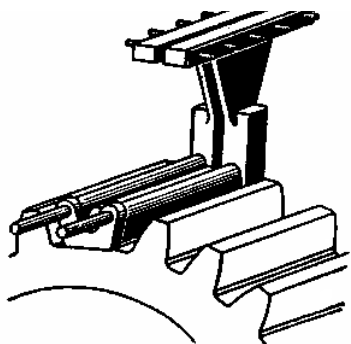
Струмонесячий провід індуктора, зігнутий за формою зуба шестерні
